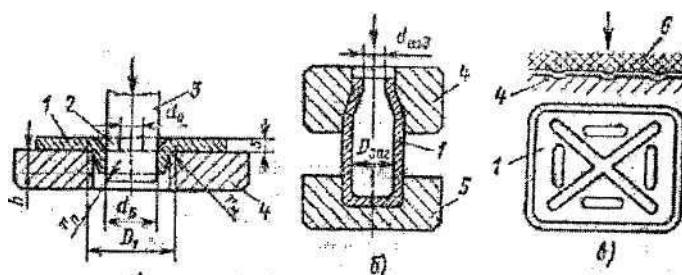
Схемы отбортовки (а), обжима (б) и формовки (в):
